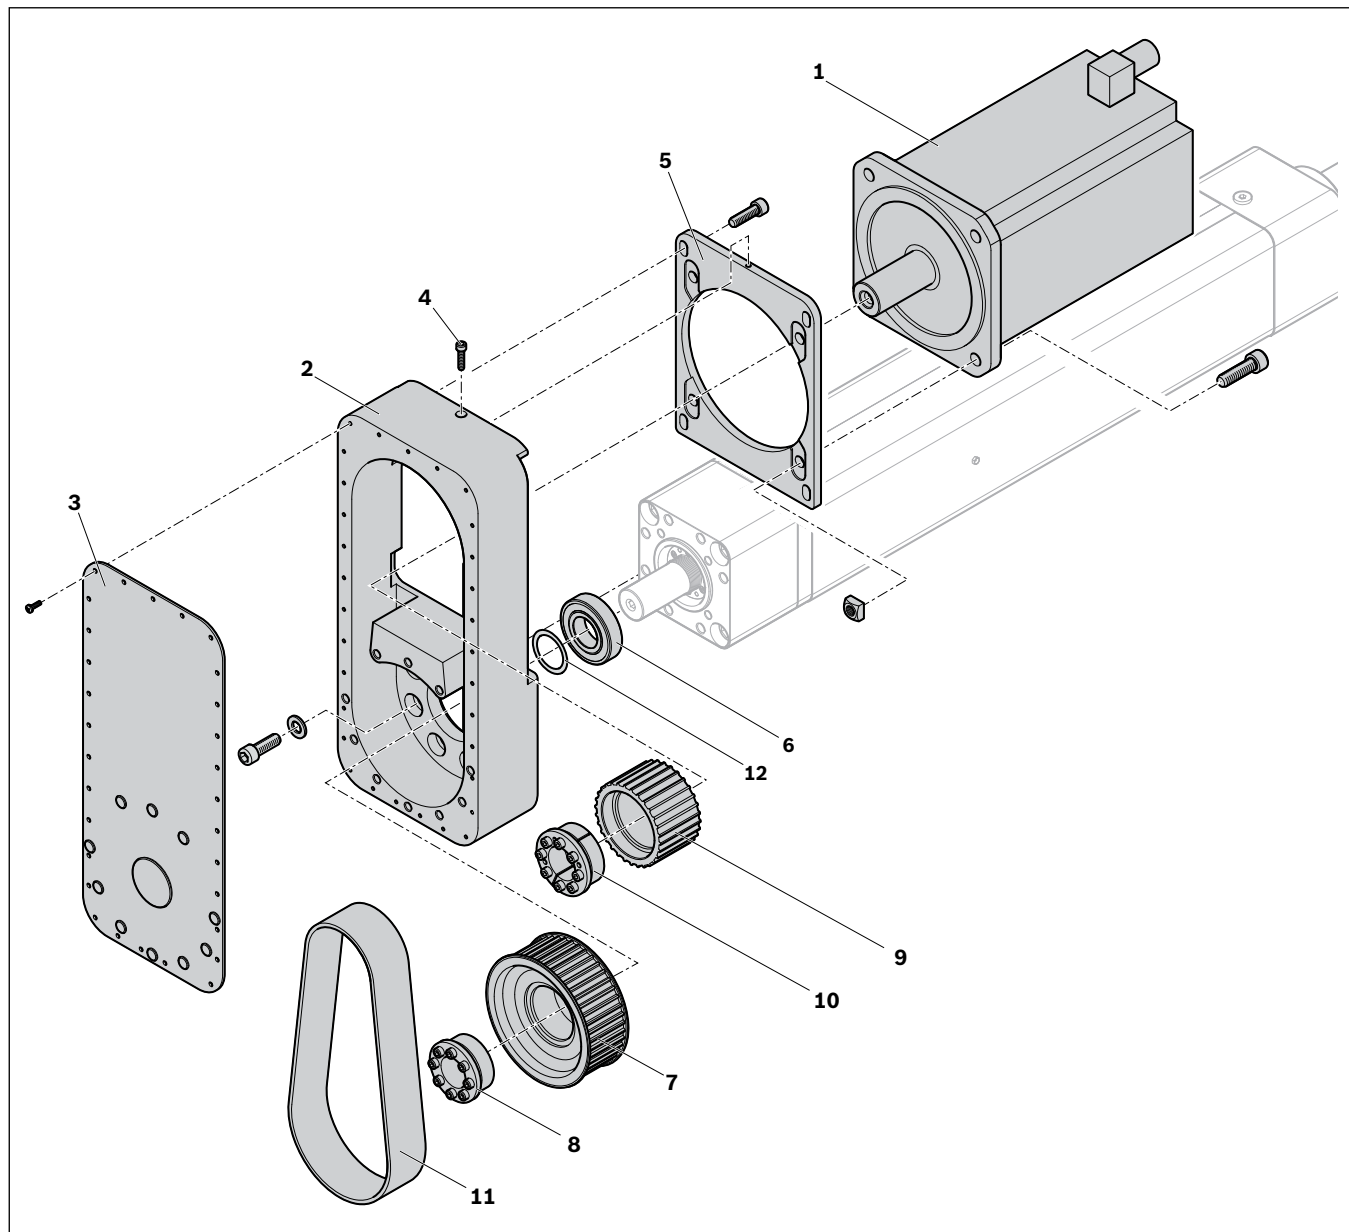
Riemenvorgelege und Motor am EMC-HP montieren
